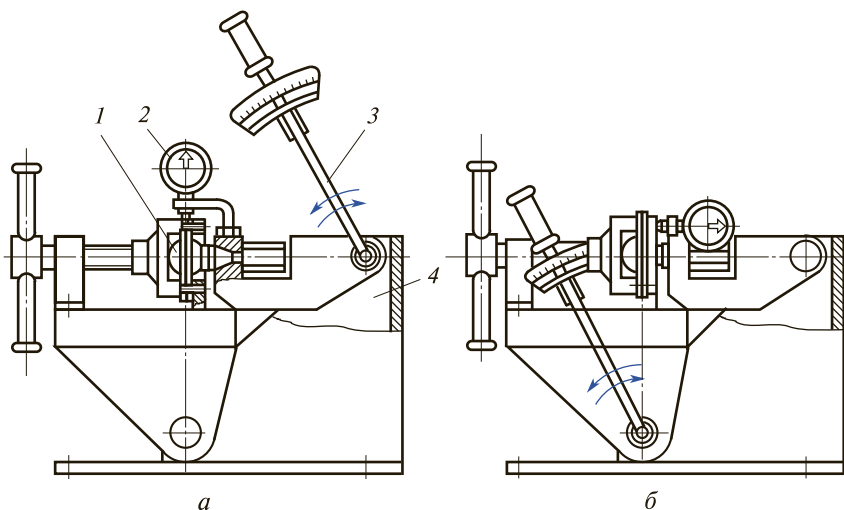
Приспособление для проверки зазоров пальца шарового шарнира:
